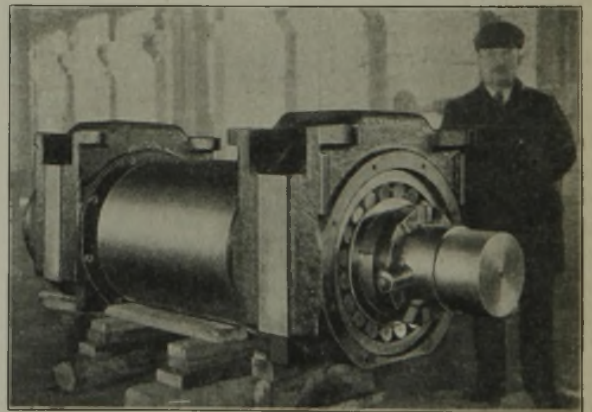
a. Walze mit Einbaustücken und Rollenlagern.
